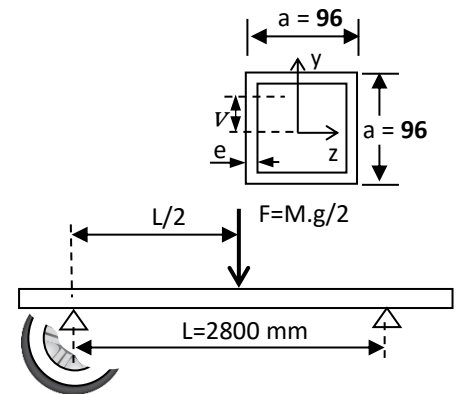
Flexion d'une poutre (longeron) sur deux appuis et section droite du profilé de la poutre
